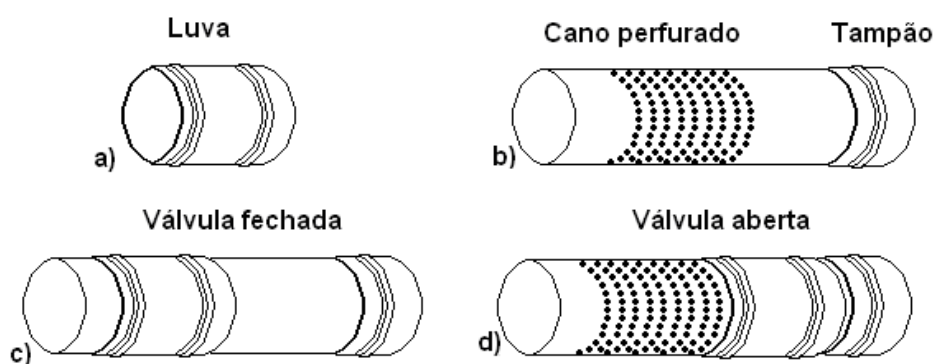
Válvula construída a partir de peças de PVC: a) Luva de Correr b) Cano perfurado com Tampão; c) Conjunto montado com válvula fechada; d) Conjunto montado com válvula aberta.
